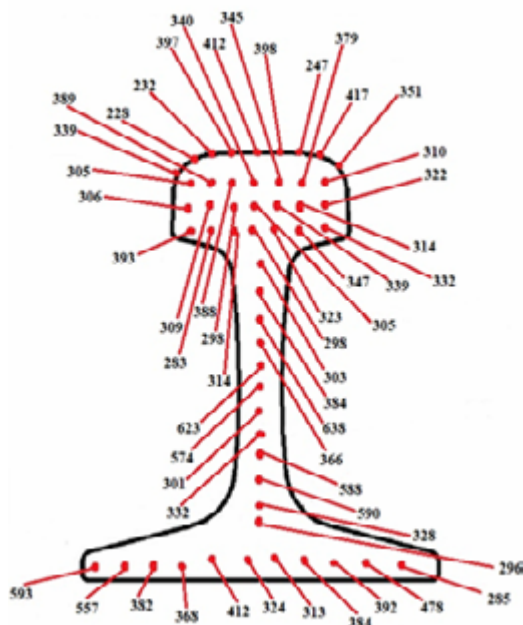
Определение твердости сварного соединения рельса Р-65 в НВ
